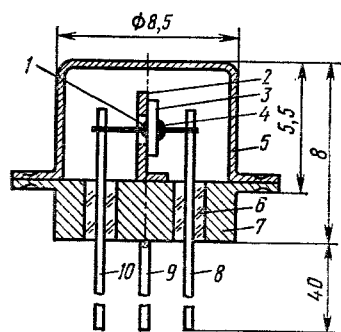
Конструкция сплавных маломощных транзисторов в корпусе с герметизацией холодной сваркой:
